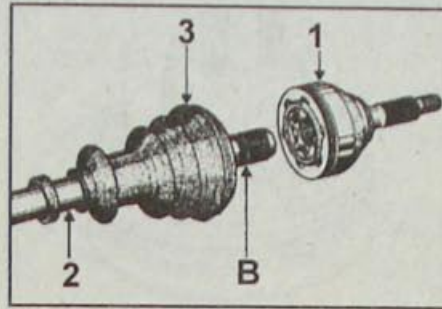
Установка шарнира равных угловых скоростей на приводной вал:
